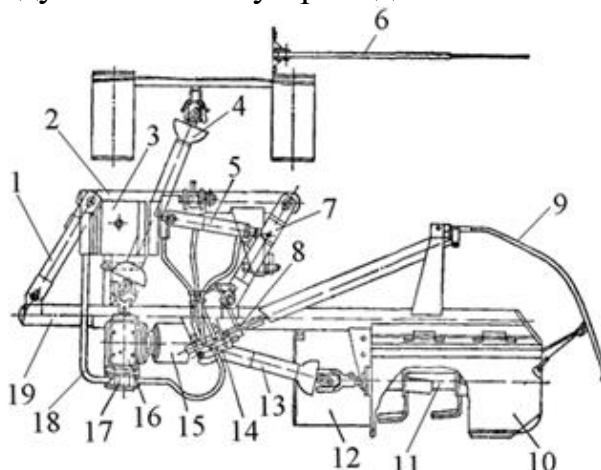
Функціональна схема фрези ФА – 0,76: 1, 7 – важелі; 2 – рама; 3 – бак для оливи; 4, 13 – вали карданні; 5 – гідроциліндр; 6 – маркер; 9 – щуп; 8 – тяга щупа; 10 – кожух фрезерного барабана; 11 – фрезерний барабан; 12 – башмак; 14 – гідророзподільник; 15 – муфта; 16 – конічний редуктор; 17 – насос; 18 – гідравлічні рукави; 19 – брус несучий
